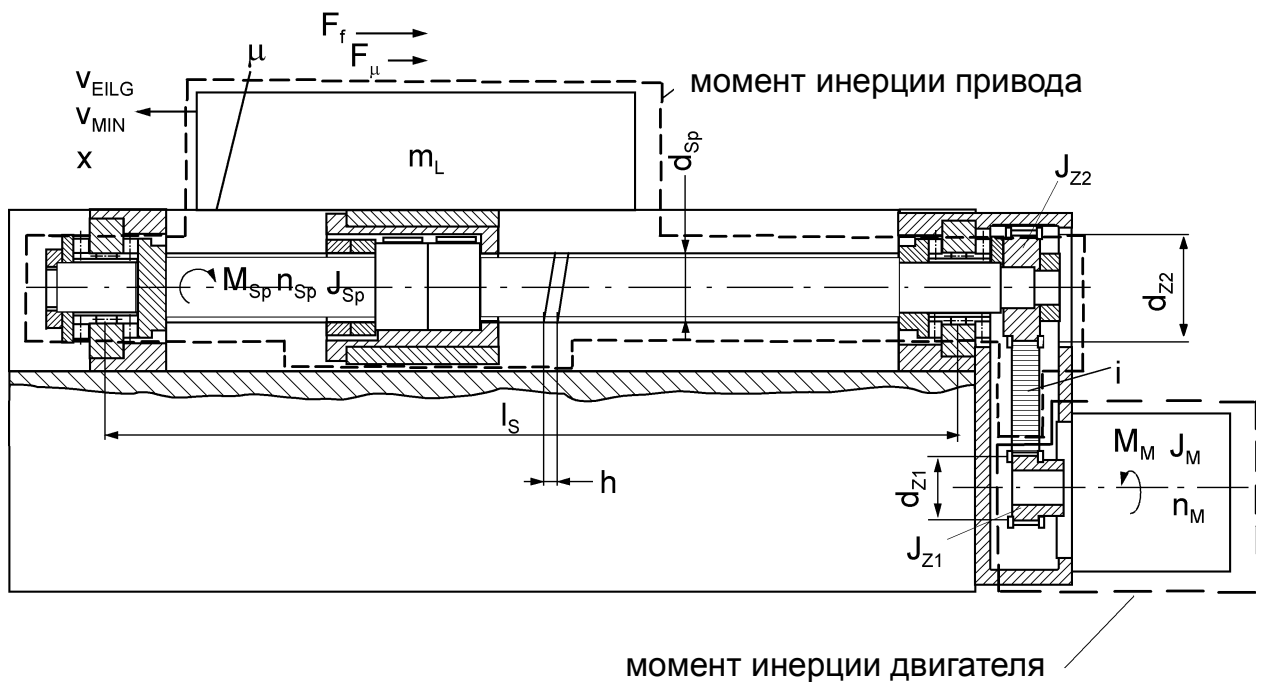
Ременный двухопорный шариковинтовой привод подачи
